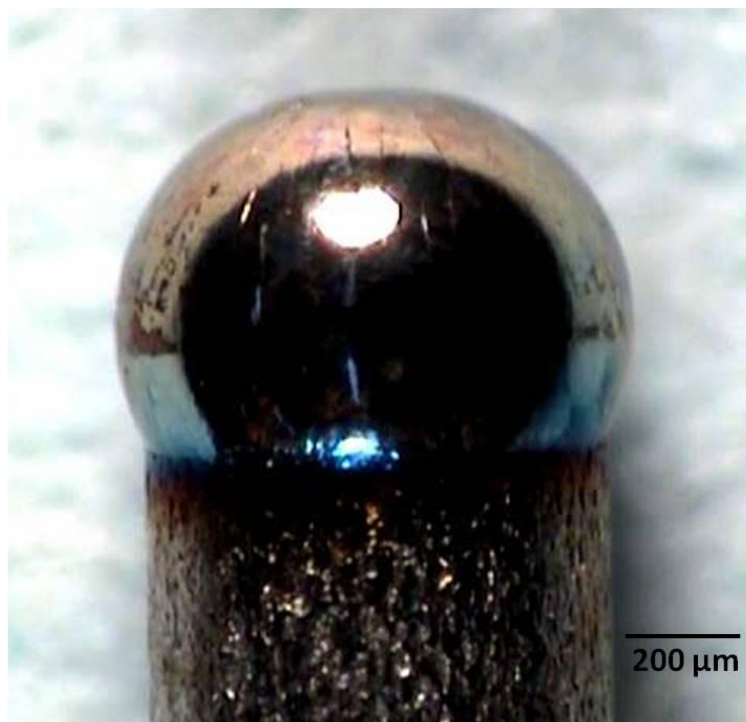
Solda com diâmetro maior que o diâmetro do tubo de titânio
